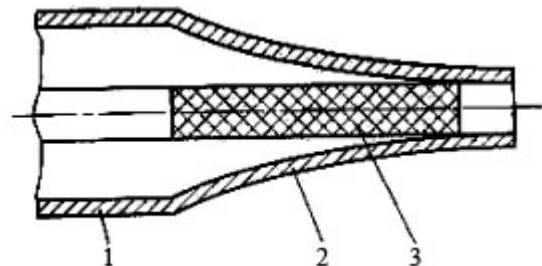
Согласованная нагрузка для коаксиального волновода: 1 – цилиндрическая часть корпуса; 2 – согласующий экспоненциальный корпус; 3 – стандартный резистор
